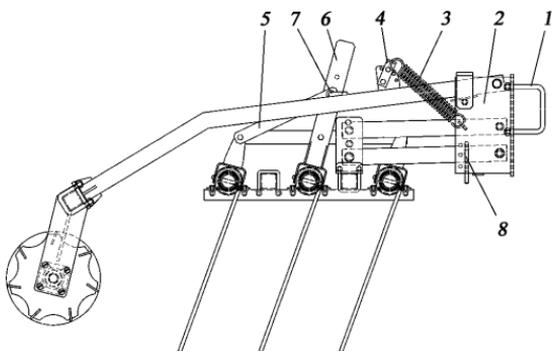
Механизмы регулировки зубовой бороны и катка
